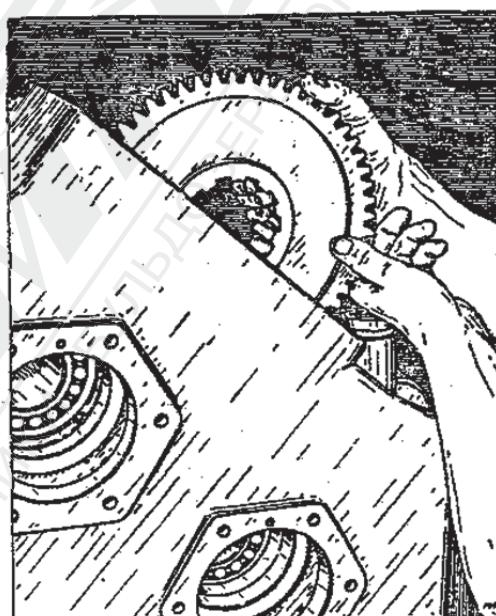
Установка зубчатого колеса I,II,III валика
